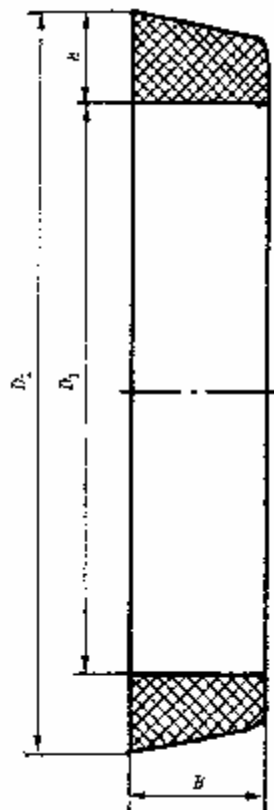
Резиновый сальниковый уплотнитель (размеры приведены в табл. 3.22)
